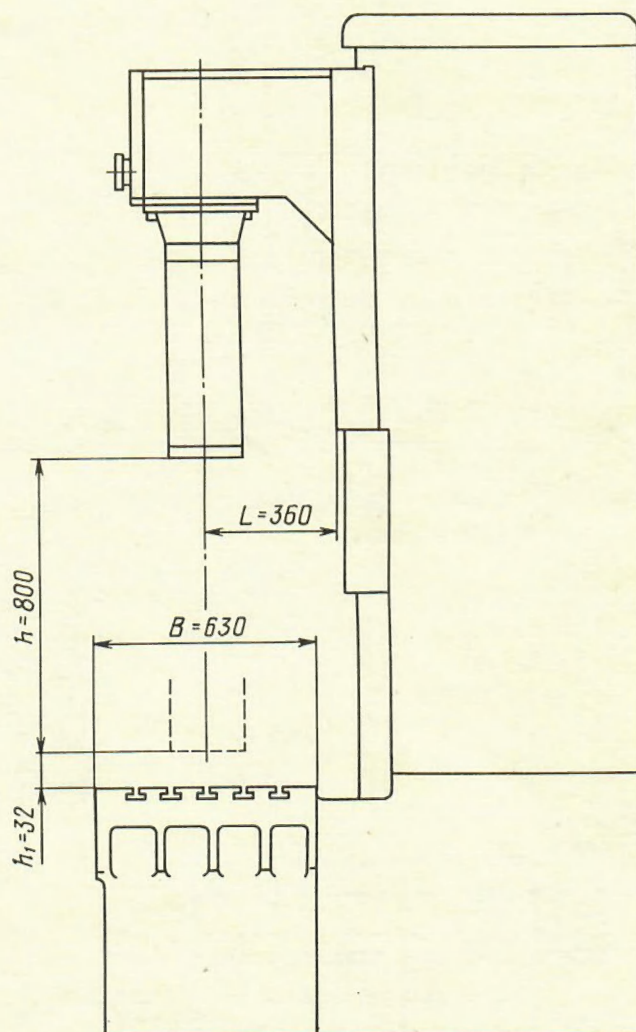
Габаритные размеры рабочего пространства станка 2733ПН
